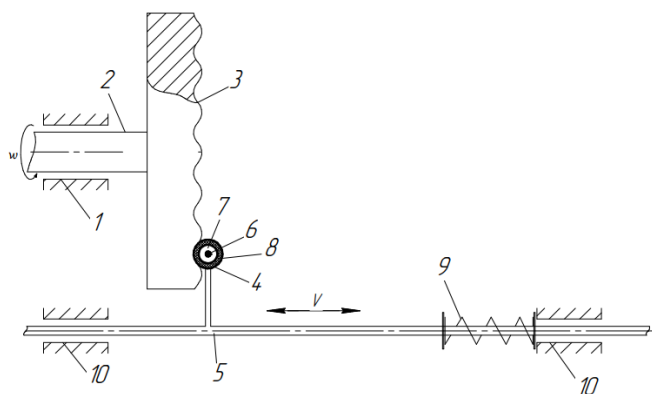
Конструкция кулачкового механизма: 1 – опора, 2 – ведущий вал, 3 – цилиндрический кулачок, 4 – ролик, 5 – толкатель, 6 – ось, 7 – металлическая втулка, 8 – резиновая втулка, 9 – пружина, 10 – направляющий
